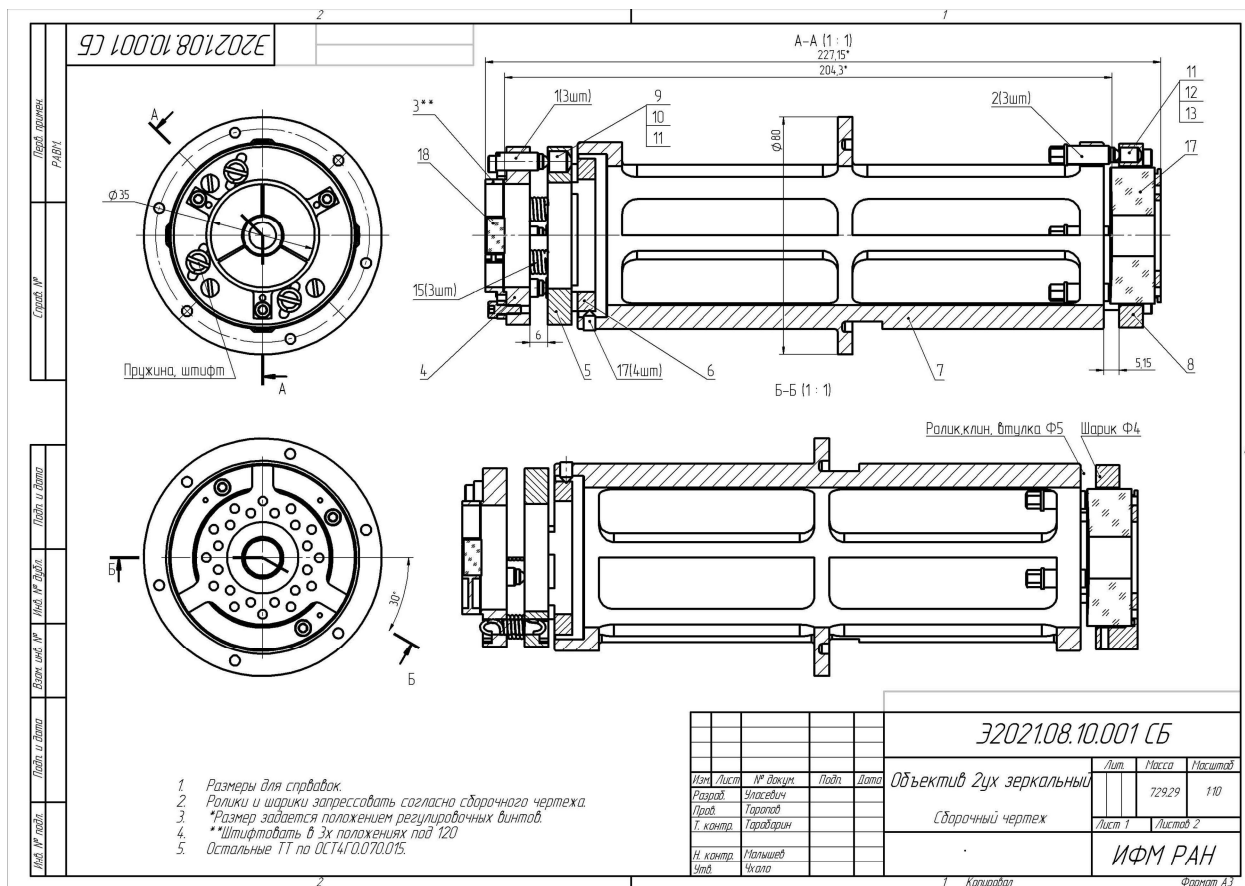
Сборочный чертеж объектива микроскопа для имиджинга лазерного факела
